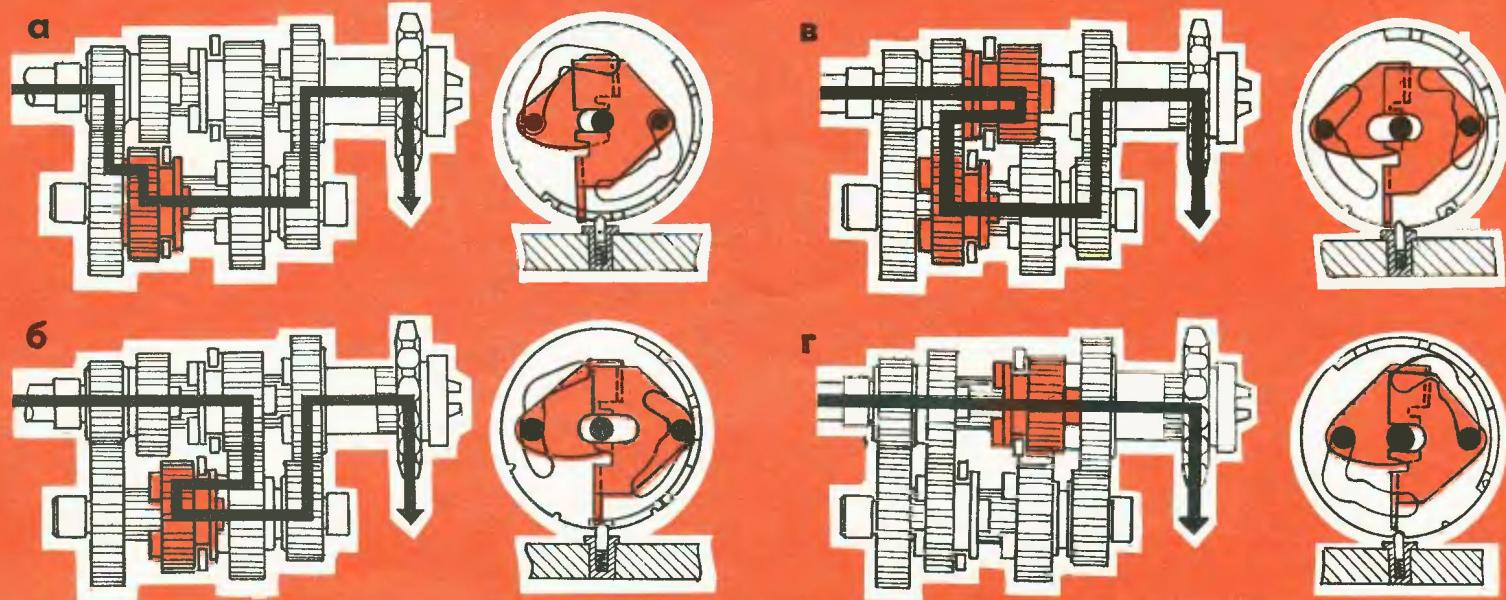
Схема положения шестерен коробки и механизма переключения (справа) при включении передач: а — первой; б — второй; в — третьей; г — четвертой.
